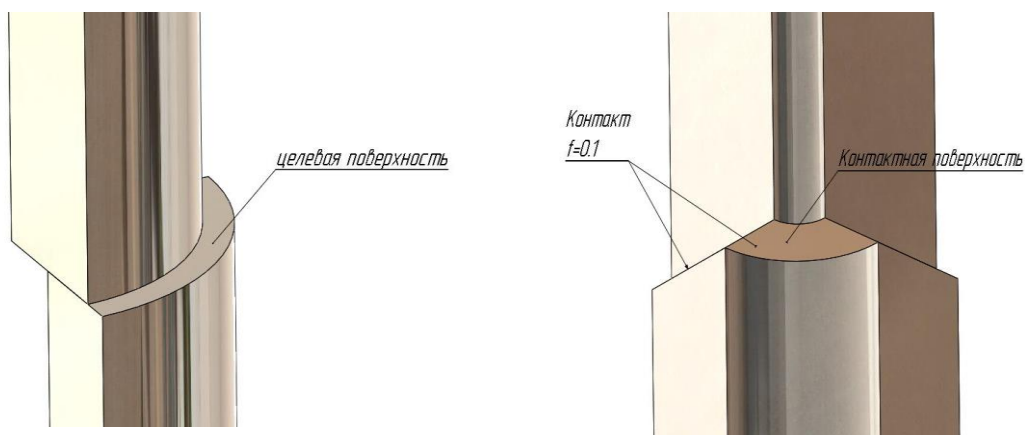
Схема- Заготовка-Опора контактных пар
